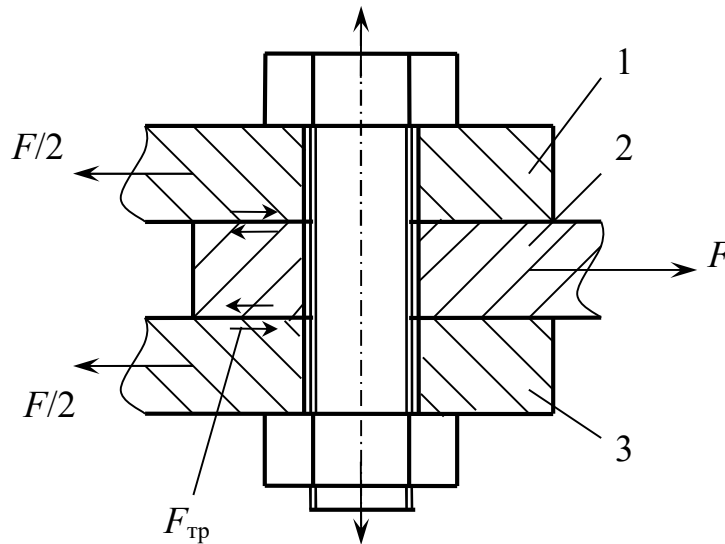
Соединение, нагруженное поперечными силами (болт в отверстиях с зазором)
